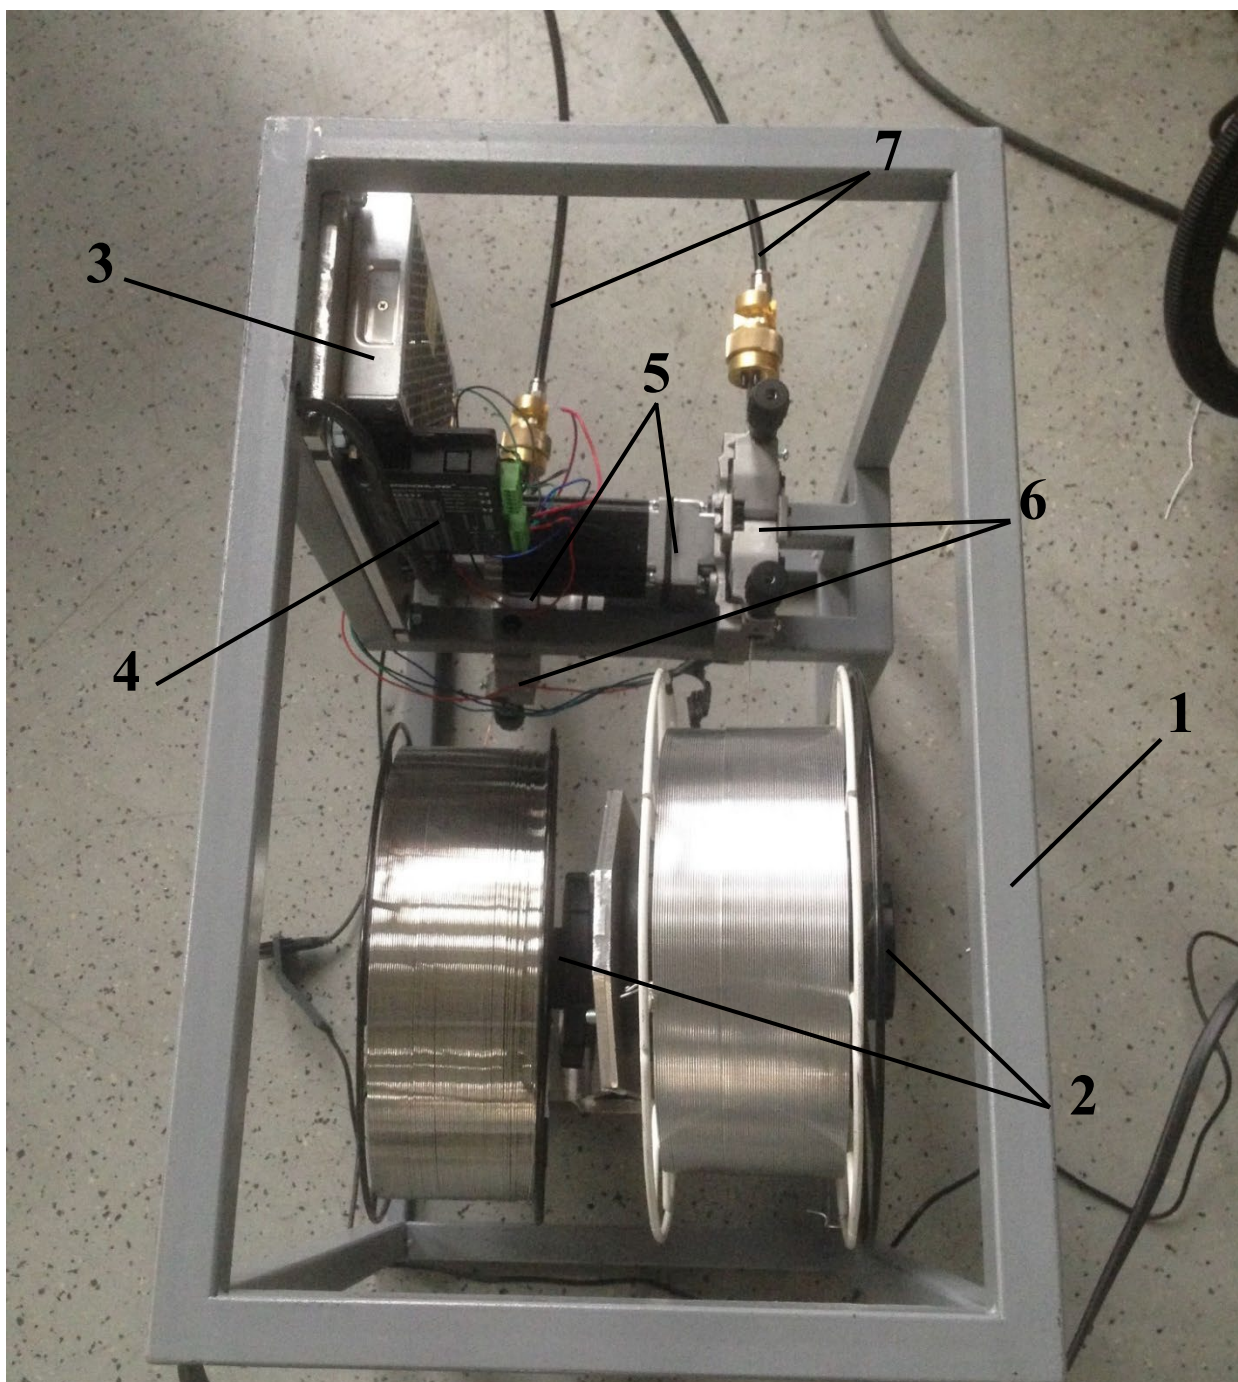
Опытная конструкция для осуществления одновременной механизированной подачи двух разнородных сварочных проволок: 1 – корпус конструкции; 2 – место установки кассеты с проволокой; 3 – блок питания; 4 – программируемый микроконтроллер; 5 – шаговый электродвигатель; 6 – механизм подачи проволоки толкающего типа; 7 – кабель канал
